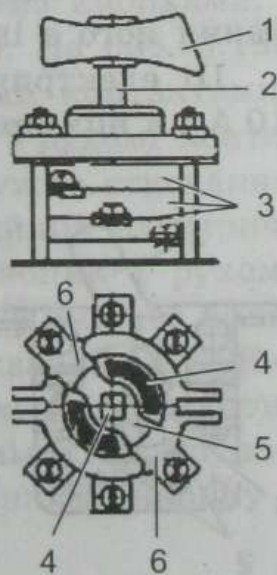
Пакетний вимикач серії ВІМ: 1 – рукоятка; 2 – вал; 3 – пакети; 4 – пластини із фібри; 5 – рухомий контакт; 6 – нерухомі контакти
